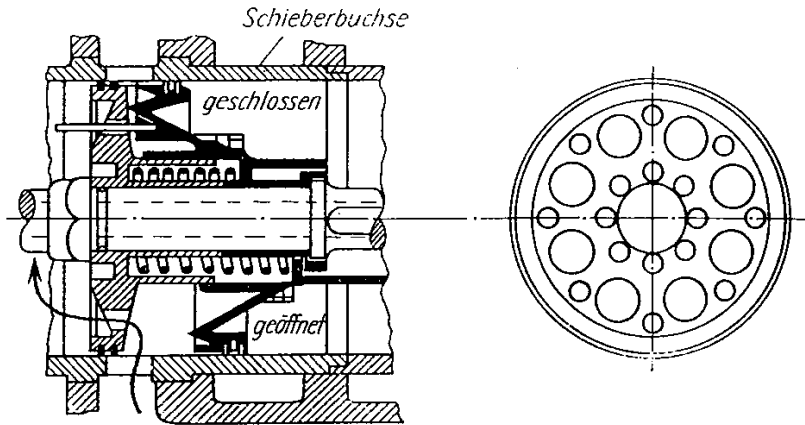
Karl-Schulz-Druckausgleich-Kolbenschieber
